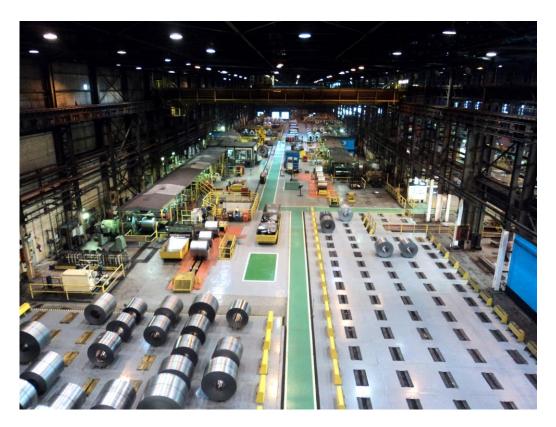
Linha de Acabamento final - Linhas de Inspeção Fonte: Arquivo Técnico Industrial – Usiminas (2016).
